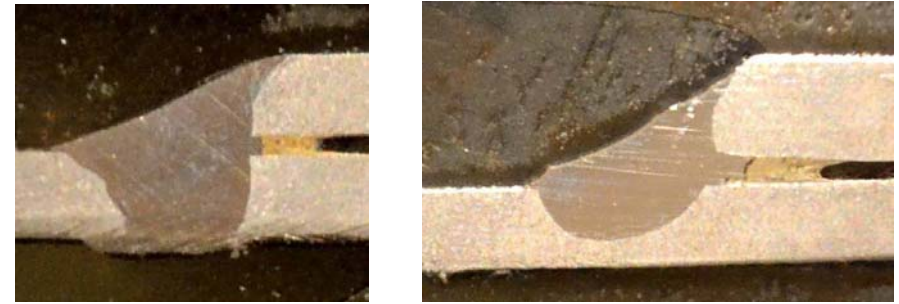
Макрошліфи паяно-зварних з'єднань
